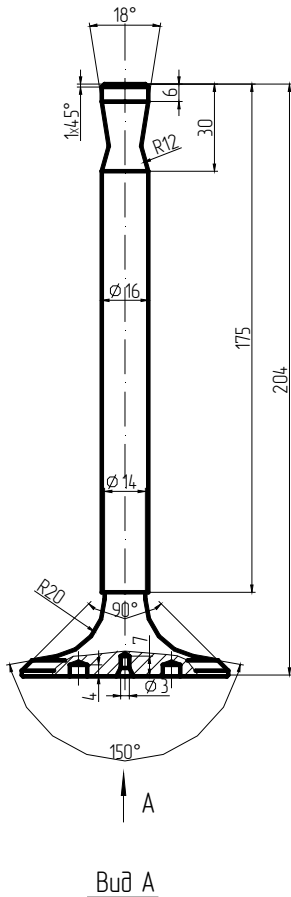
Конструктивна схема випускного клапана двигуна 6ЧСПН18/22
